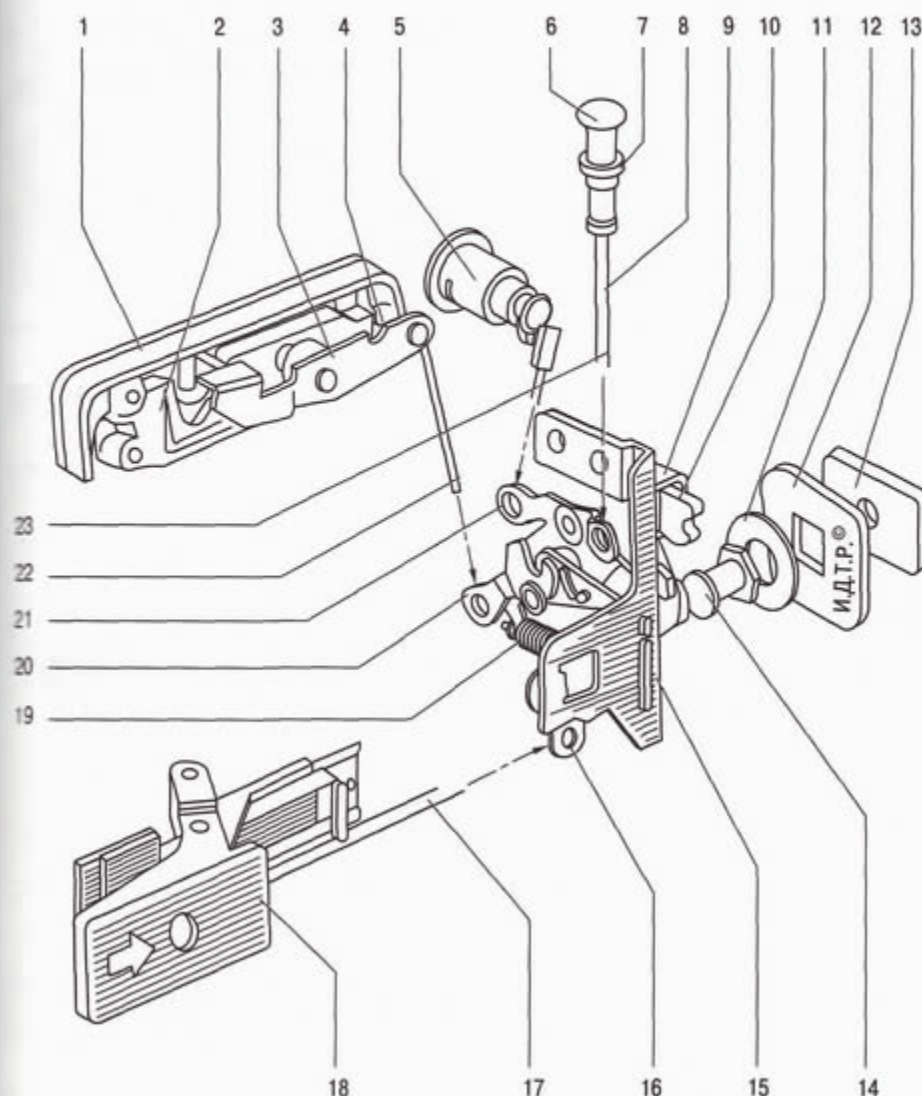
Замок правой боковой двери и его приводы: 1 – наружная ручка; 2 – основание ручки; 3 – рычаг ручки; 4 – пружина; 5 – выключатель замка; 6 – кнопка; 7 – розетка; 8 – тяга кнопки; 9 – крышка замка; 10 – вилчатый ротор; 11 – шайба фиксации замка; 12 – панель кузова; 13 – пластина фиксатора; 14 – фиксатор замка; 15 – замок двери; 16 – рычаг привода внутренней ручки; 17 – тяга внутренней ручки; 18 – внутренняя ручка; 19 – пружина рычага запирания замка; 20 – рычаг привода наружной ручки; 21 – двуплечный рычаг включения замка; 22 – тяга наружной ручки; 23 – тяга выключателя замка
